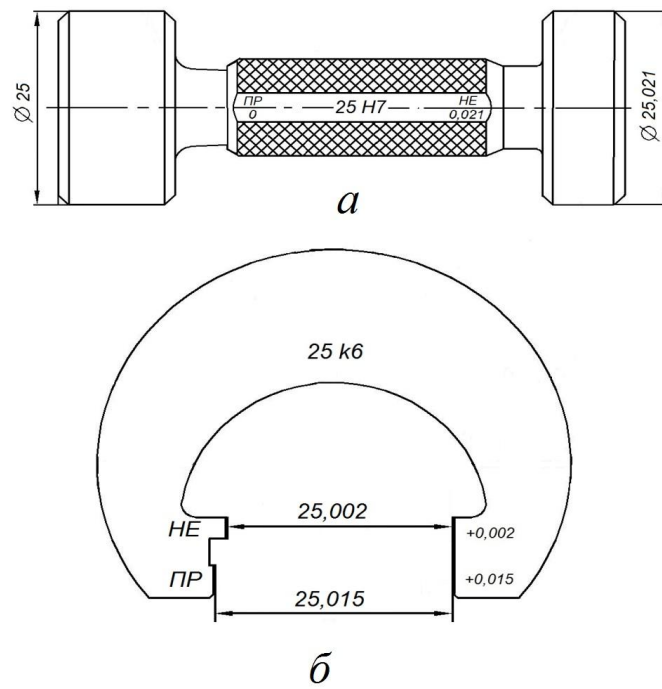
Предельные калибры для гладких цилиндрических поверхностей
